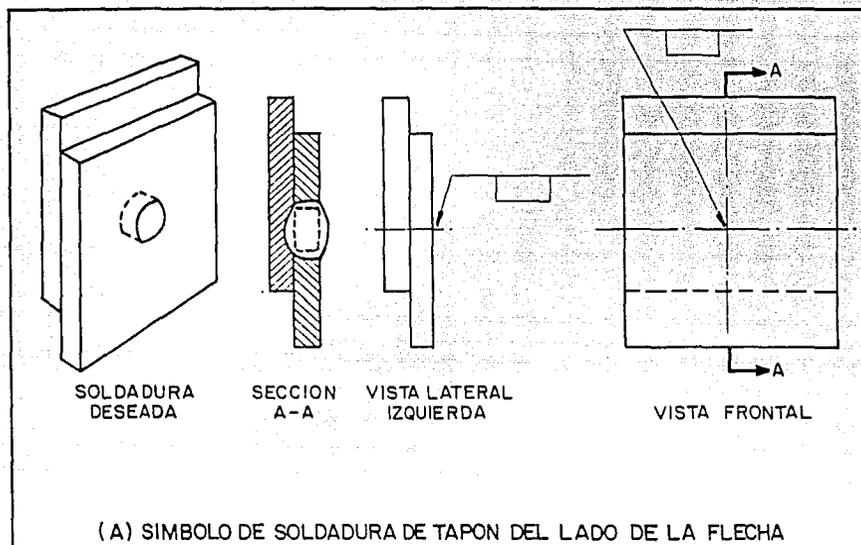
APLICACION DEL SIMBOLO DE SOLDADURA DE TAPON
